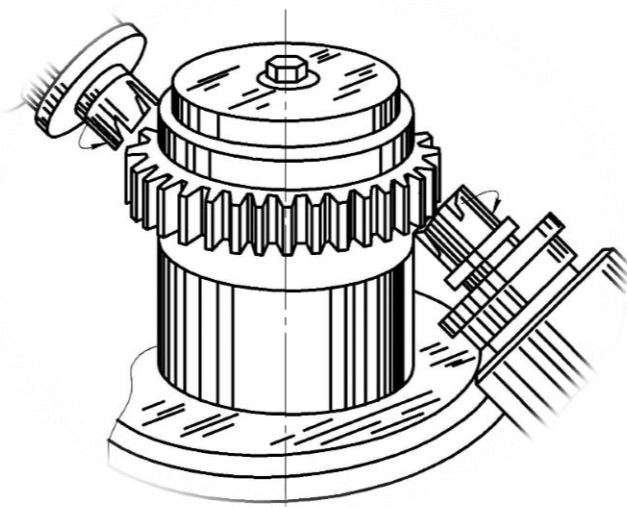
Верстат для заокруглення зубів двома чашковими фрезами
